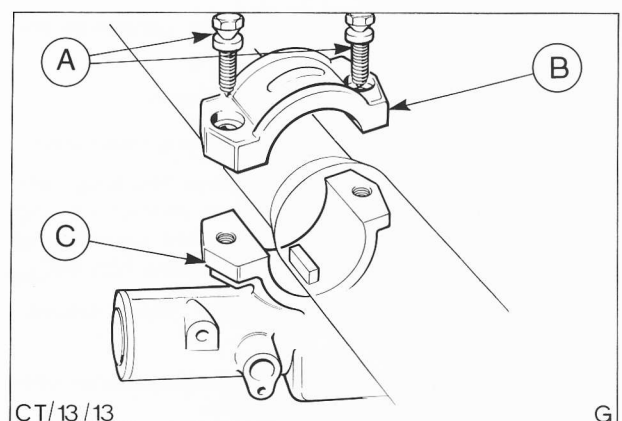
A = Befestigungsschrauben (Abscherbolzen)
